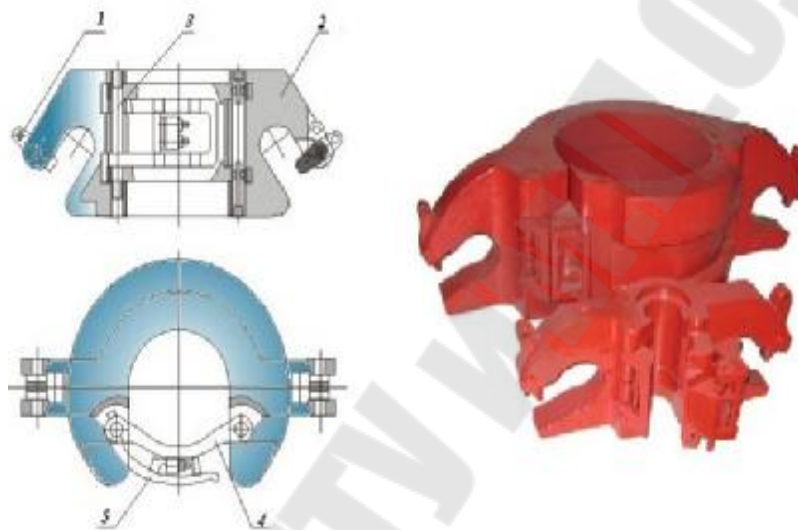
Элеваторы: 1-фиксатор; 2-корпус; 3- ось шарнира; 4-дверца; 5-ручка
